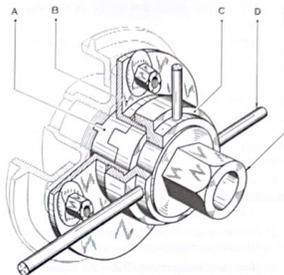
Utilización de la llave 3301-T para desenroscar o enroscar el anillo-tuerca del tambor de rueda trasero.
